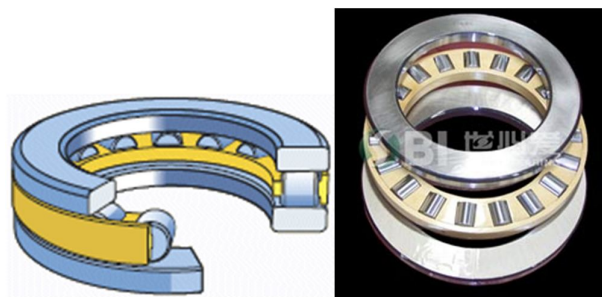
39.- Rodamientos de rodillos cilíndricos de empuje.
